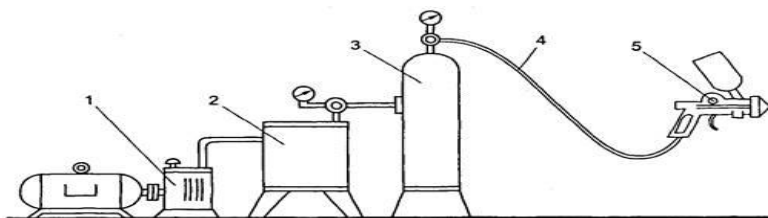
Схема установки для пневматического распыления: 1 — компрессор; 2 — маслоотделитель; 3 — ресивер; 4 — гибкий шланг; 5 — краскораспылитель
